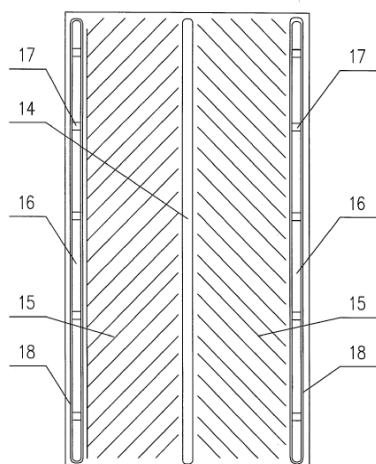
Попарно сваренные пластины разборной греющей камеры
